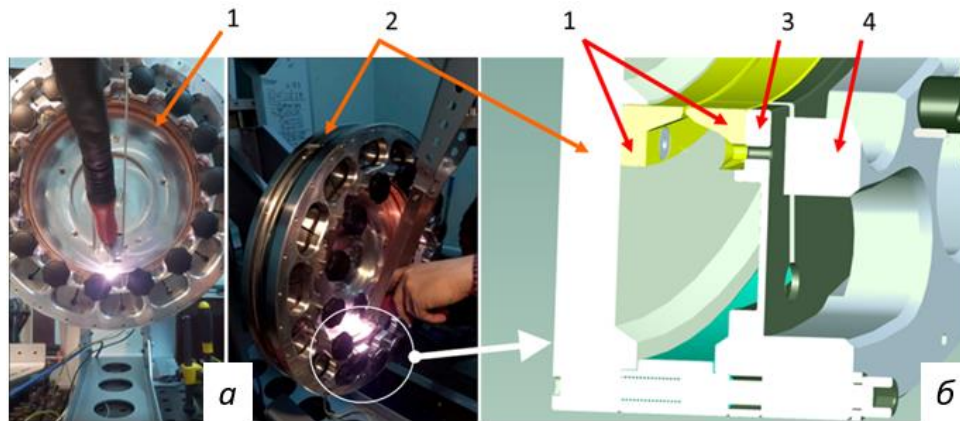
Оснащення установки в процесі зварювання внутрішнього кільцевого шва (а) та розріз зони фіксації та зварювання шва (б)
